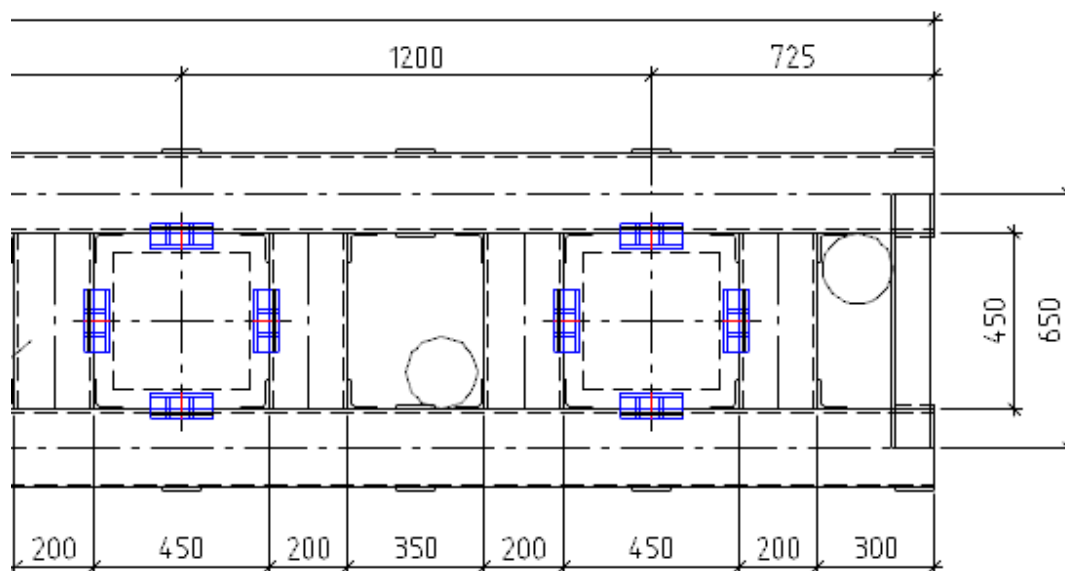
Чертеж нового кондуктора (вид сверху)
